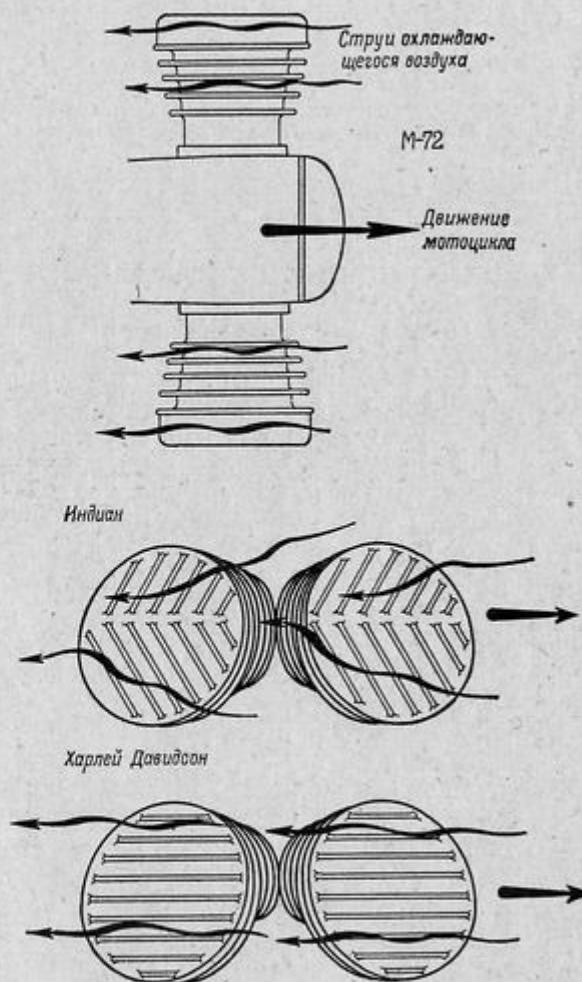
Схема обдува двухцилиндровых двигателей при воздушном охлаждении.
